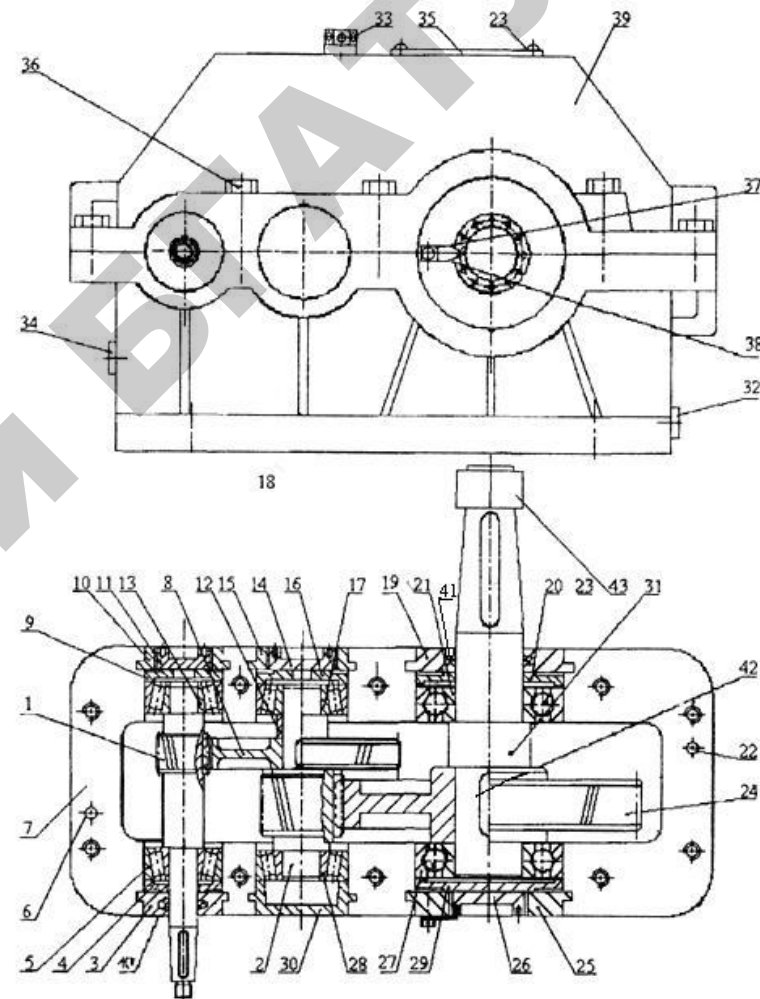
Двухступенчатый цилиндрический редуктор
